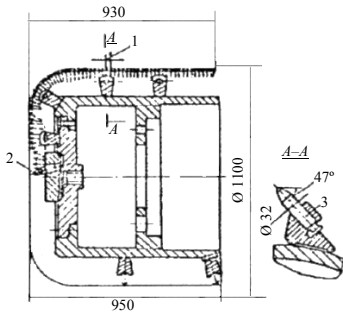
Конструкция резцовых цилиндрических барабанов под резцы типа РПП-2 и тангенциальные резцы РКС-2
